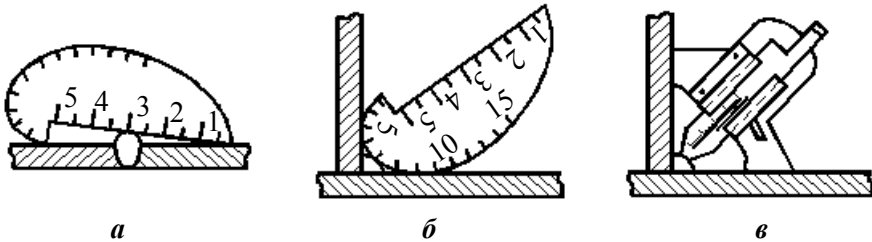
Використання шаблонів для контролю розмірів зварних швів: контроль висоти стикового шва (*а*) та катета кутового шва (*б*) універсальним шаблоном; контроль катета кутового шва шаблоном Ушєрова–Маршакєва (*в*)
